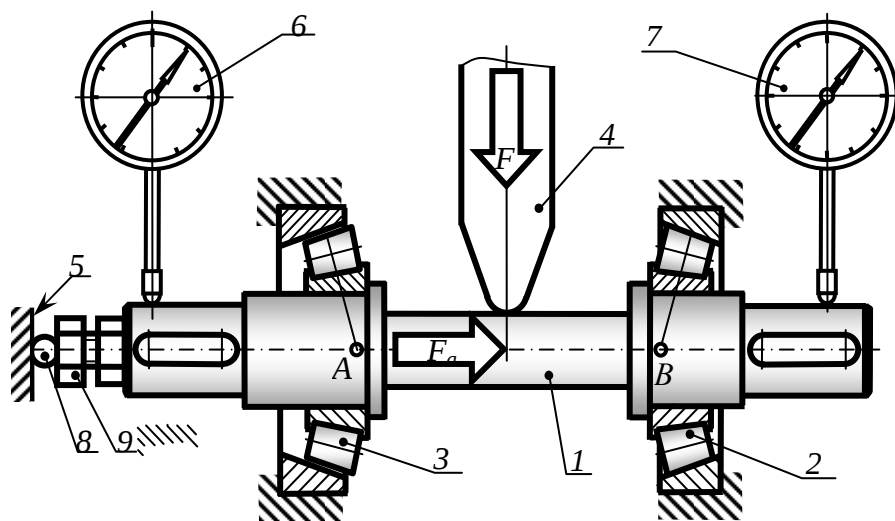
Схема нагружения экспериментального образца быстроходного вала цилиндрического косозубого редуктора: 1 – исследуемый образец вала; 2 – фиксирующая опора; 3 – поддерживающая опора; 4 – толкатель; 5 – колонна прессы ДМ-30С; 6, 7 – индикаторы; 8 – шарик; 9 – упор
